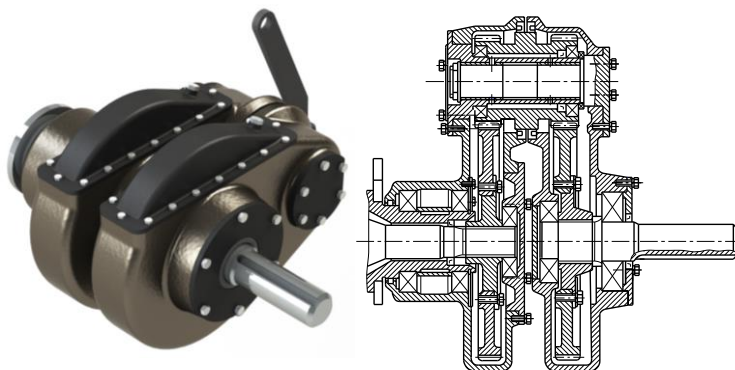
Сдвоенный бортовой редуктор для стабилизации остова трактора в поперечной плоскости
